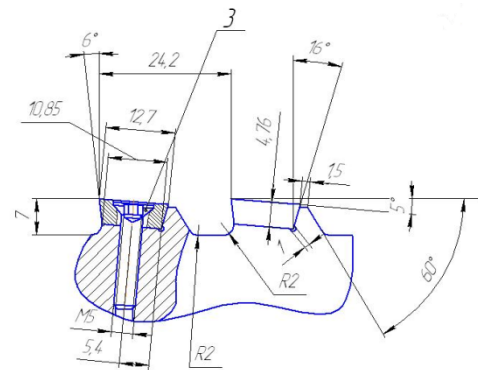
Схема крепления многогранной сменной пластинки на корпусе протяжки и общий вид сборной протяжки для обработки замка лопатки
